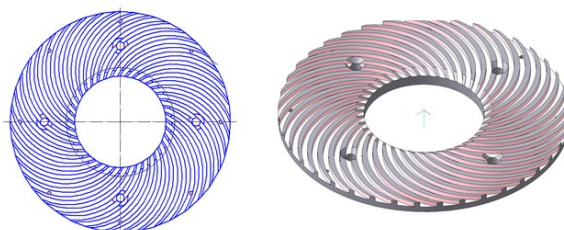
Ножевая гарнитура для размола волокнистых полуфабрикатов с криволинейной формой ножей
